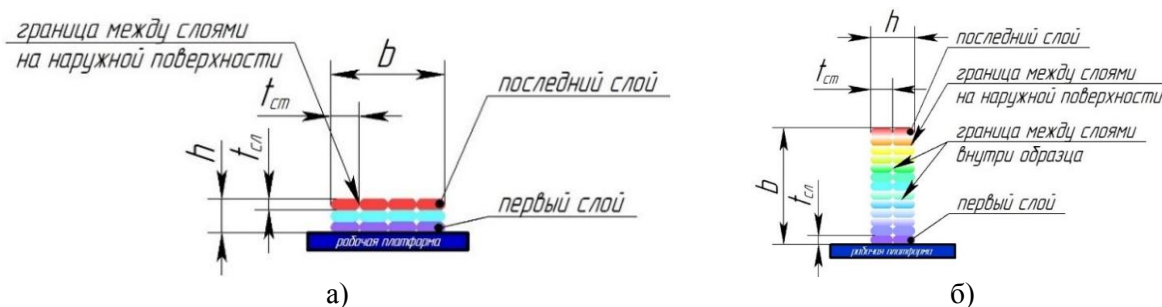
Схема расположения образца размером h_д×t_д при 3D-печати на рабочей платформе: а) ориентация образца 0°; б) ориентация образца 90°
